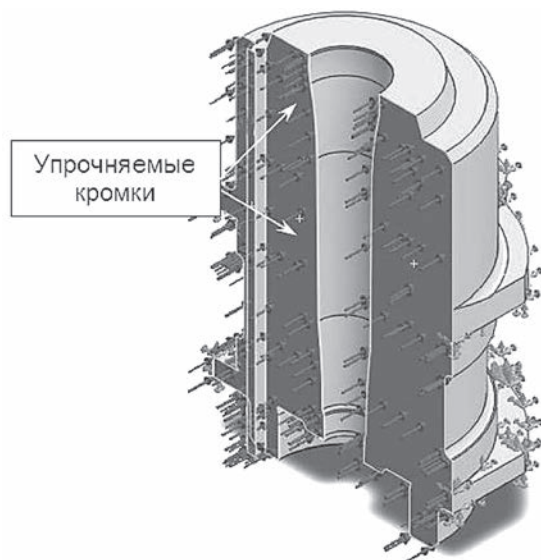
Схема ударной нагрузки на кромки деталей стеклоформ, применяемых на стеклоавтомате ВВ-7
